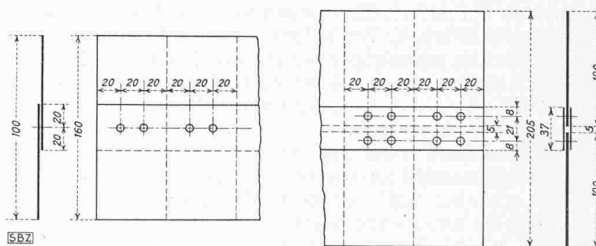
Ausführung von Schweissproben, links A, rechts B
